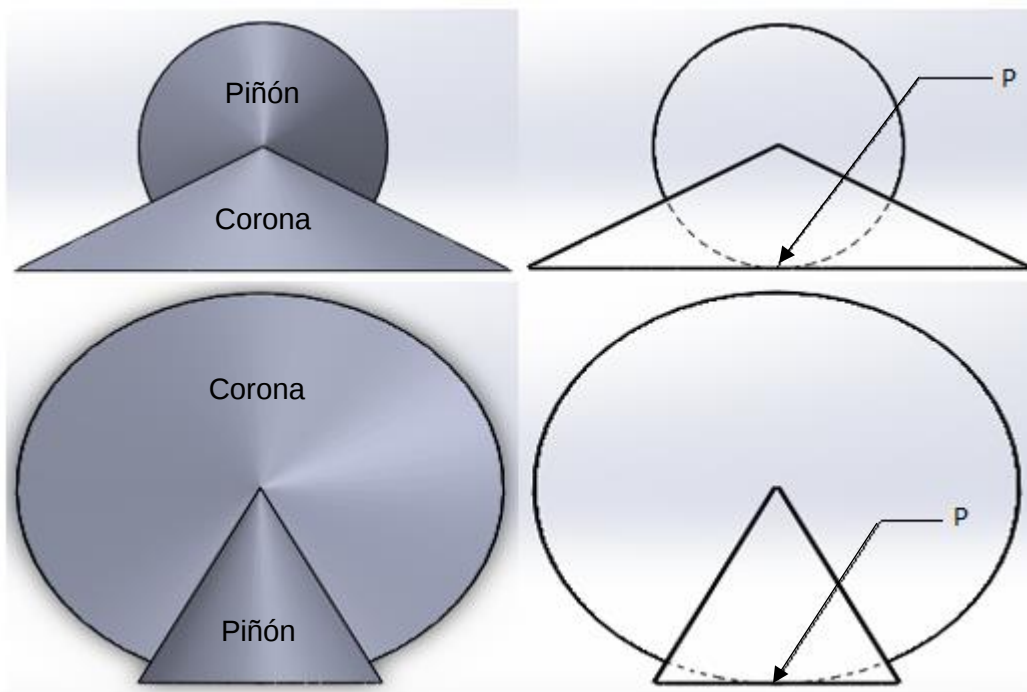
Cono de paso engranaje cónico espiral vista frontal y superior. Fuente: Autor.
